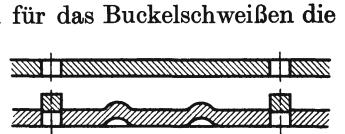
Zentrierbutzen sichern die Lage der Teile während des Buckelschweißens.
